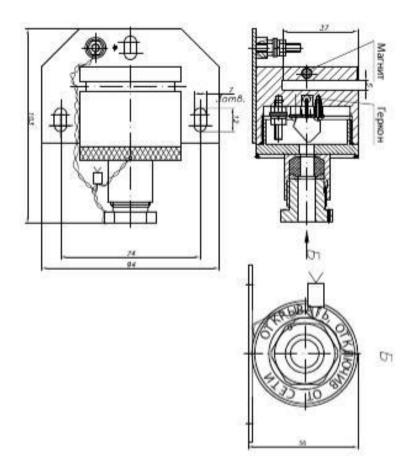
Габаритные и присоединительные размеры МГДУ КП модели 04.
